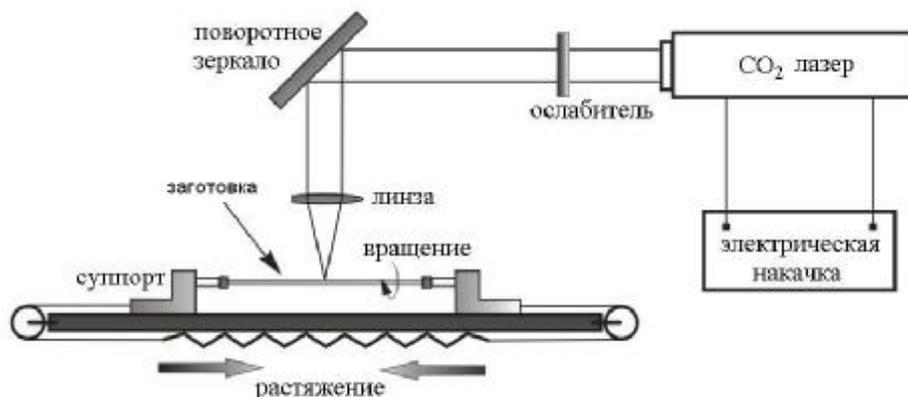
Схема лазерной установки для вытяжки с вращением заготовки [1]
